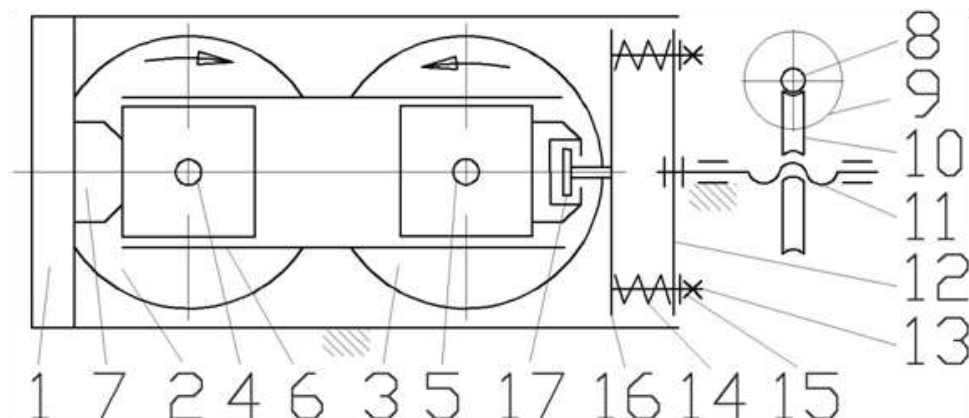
Схема установочного механізму плющильного верстата.
